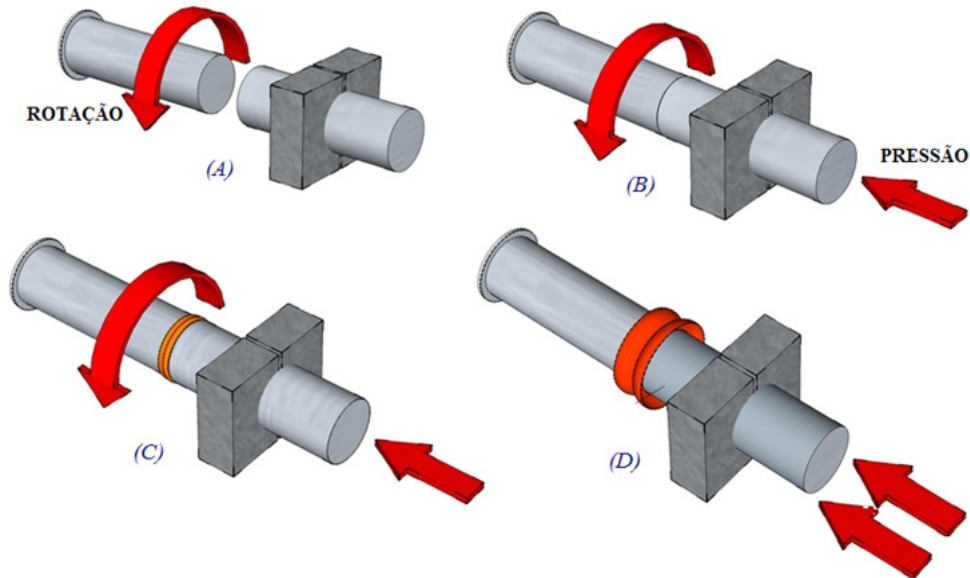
Processo de solda por fricção<sup>(21)</sup>.
